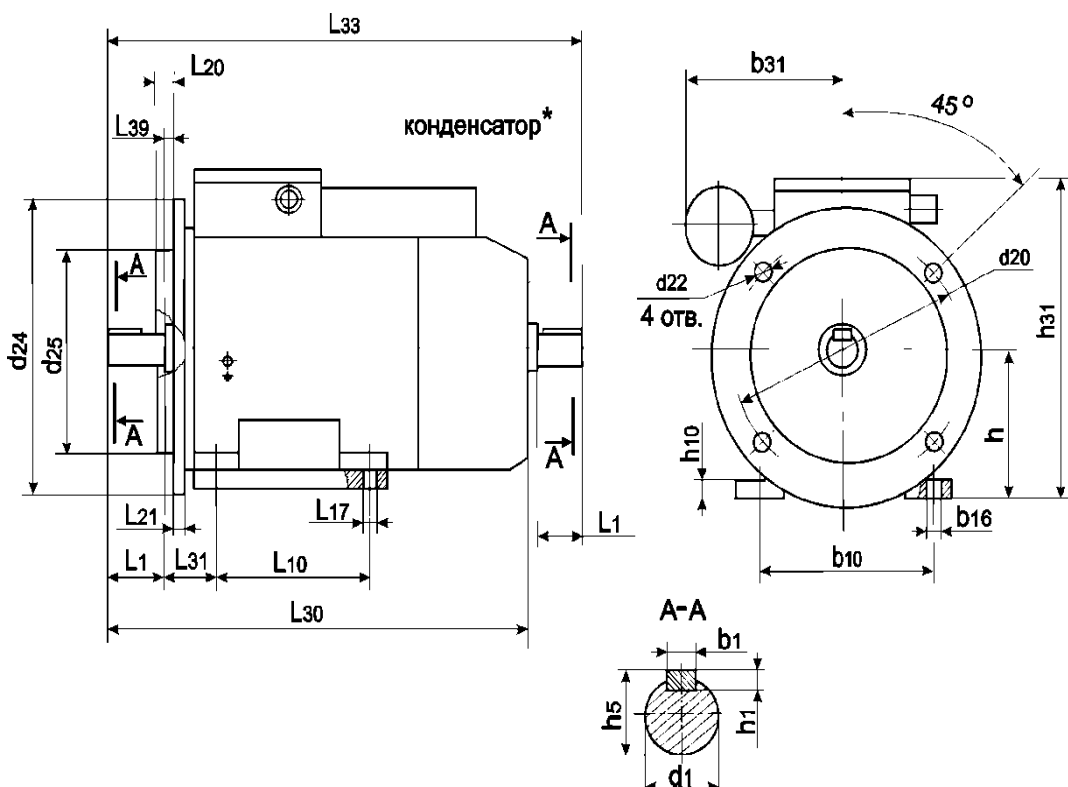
Габаритные и присоединительные размеры двигателя
